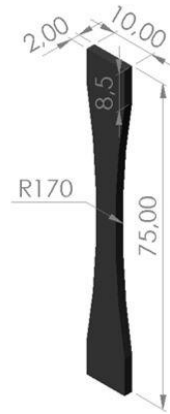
Éprouvette haltère utilisée pour le vieillissement accéléré et les essais de fatigue (dimensions en mm)
